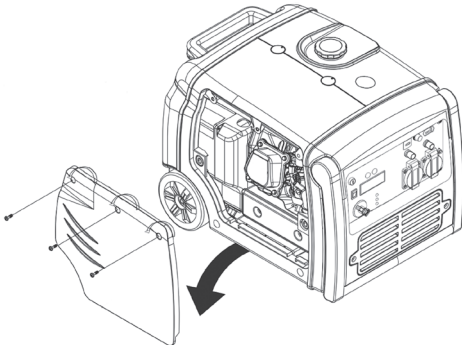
Removendo a tampa de manutenção do filtro de ar
